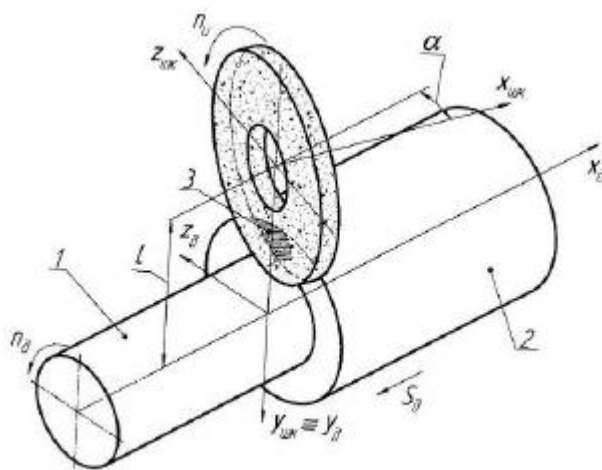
Спосіб шліфування зі схрещеними осями інструмента та деталі
